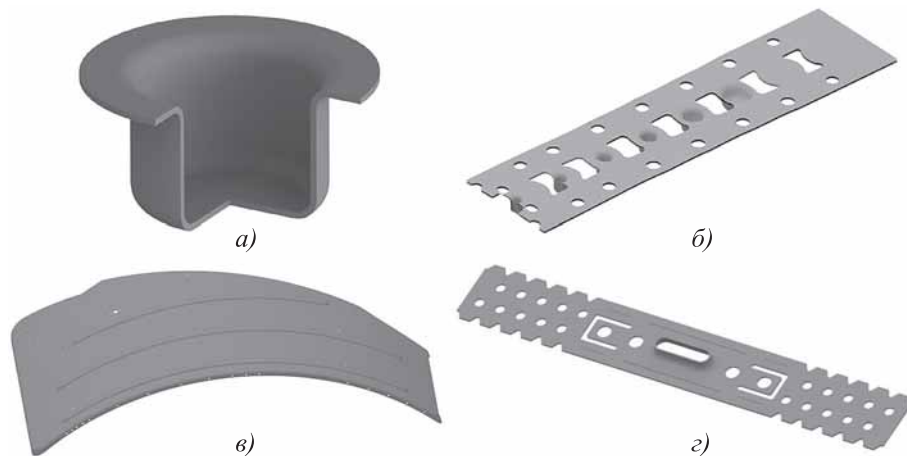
Машиностроительные 3D-модели деталей, изготавливаемых методами листовой штамповки:
